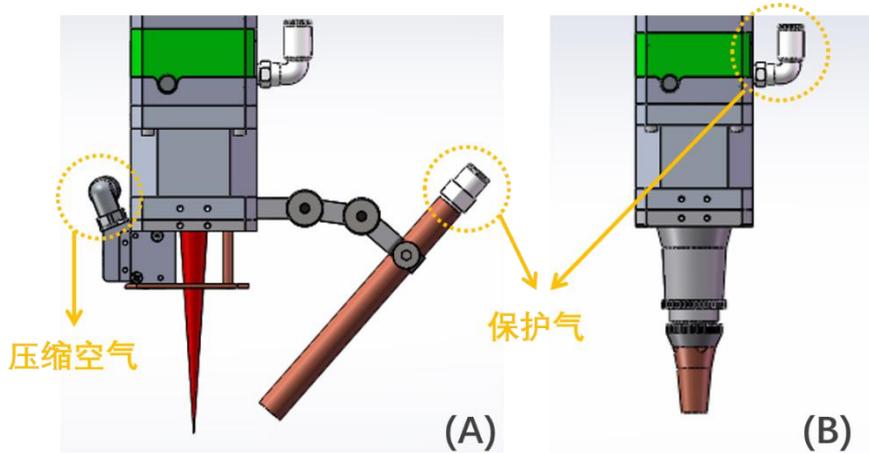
BW290 双波段激光焊接头气路接法
